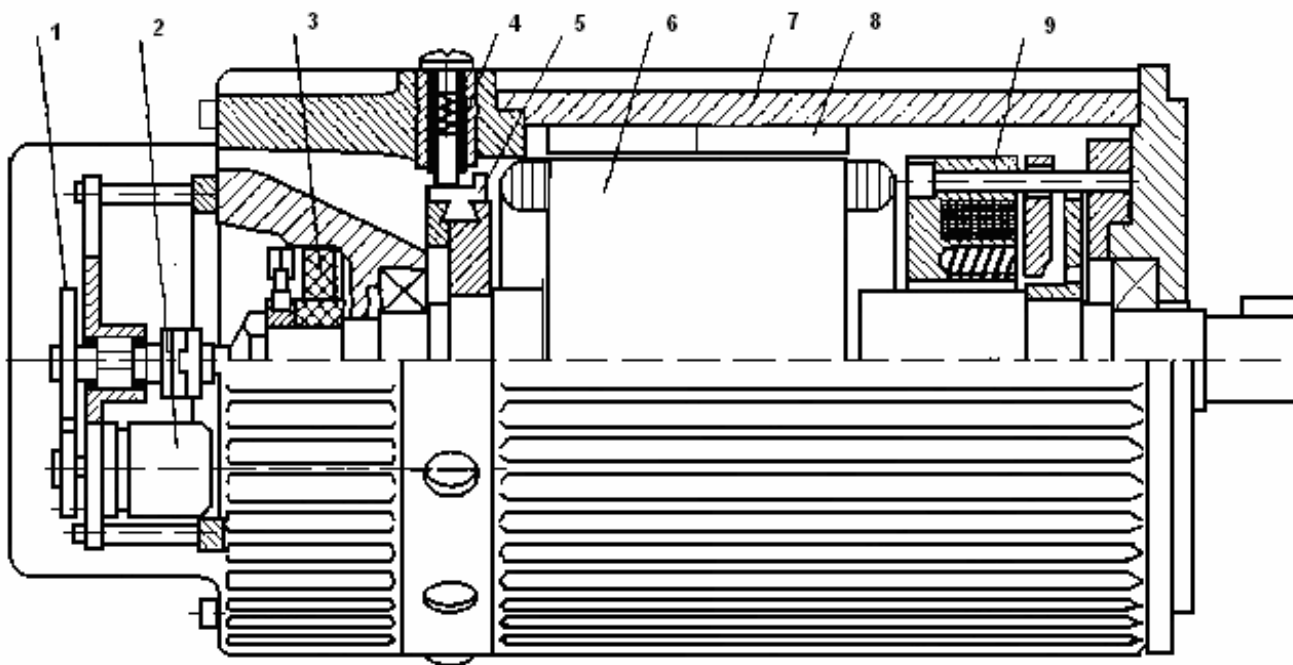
Устройство высокомоментного двигателя: 1- механическая повышающая передача; 2- револьвер; 3- тахогенератор; 4- щетки; 5- коллектор; 6- якорь; 7- цилиндрический корпус; 8- ферритовые сегменты; 9- электромагнитный тормоз.
